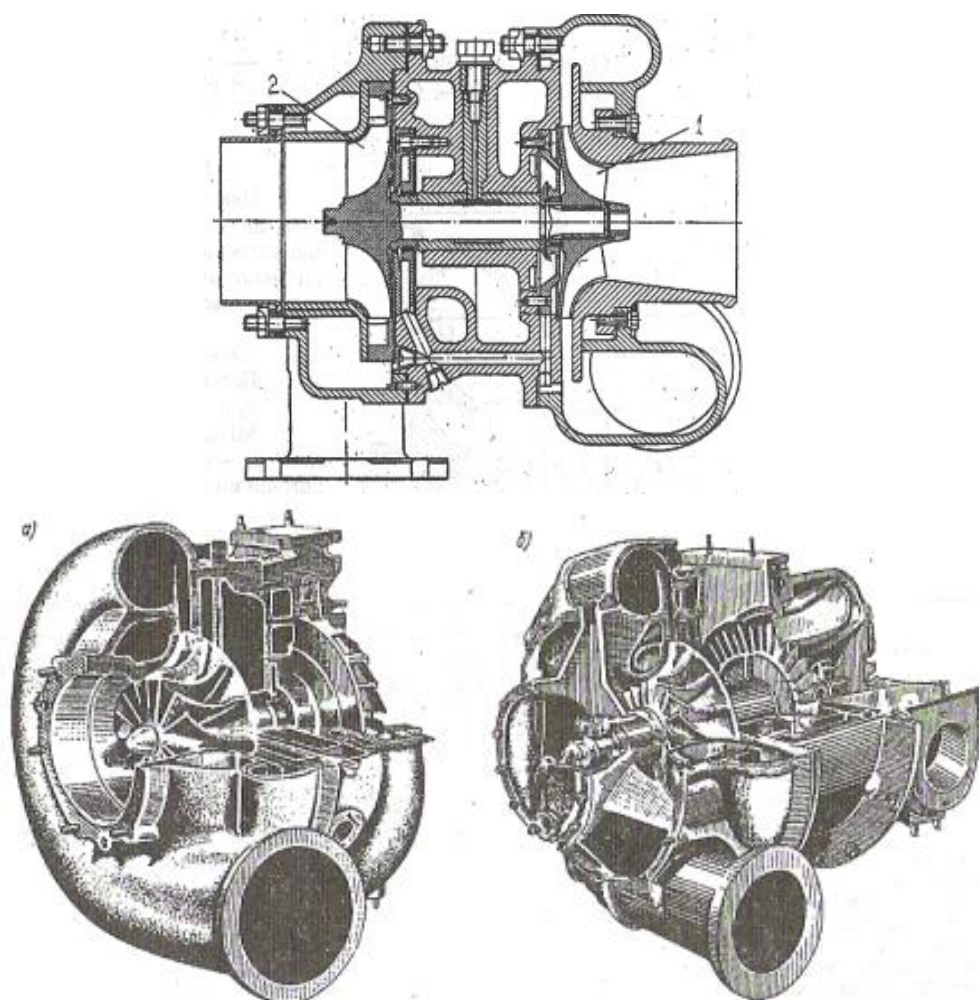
Вверху – продольный разрез агрегата турбонаддува двигателя внутреннего сгорания типа ТКР (радиальная турбина, вращающаяся выхлопными газами двигателя – слева)
